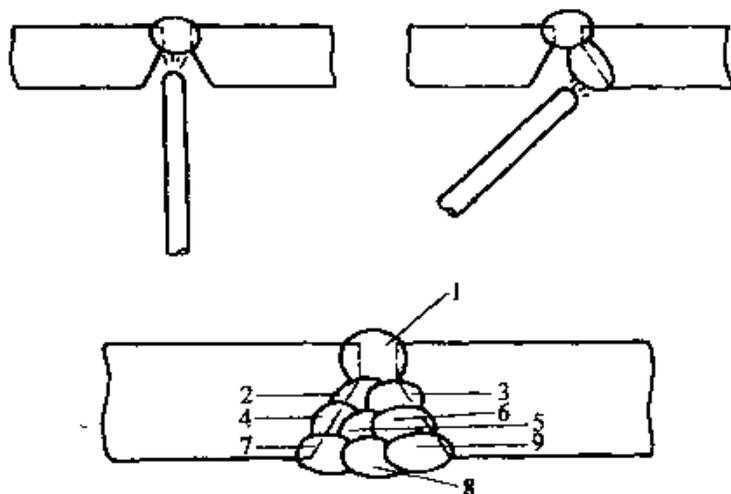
开坡口对接仰焊缝的多层多道焊
